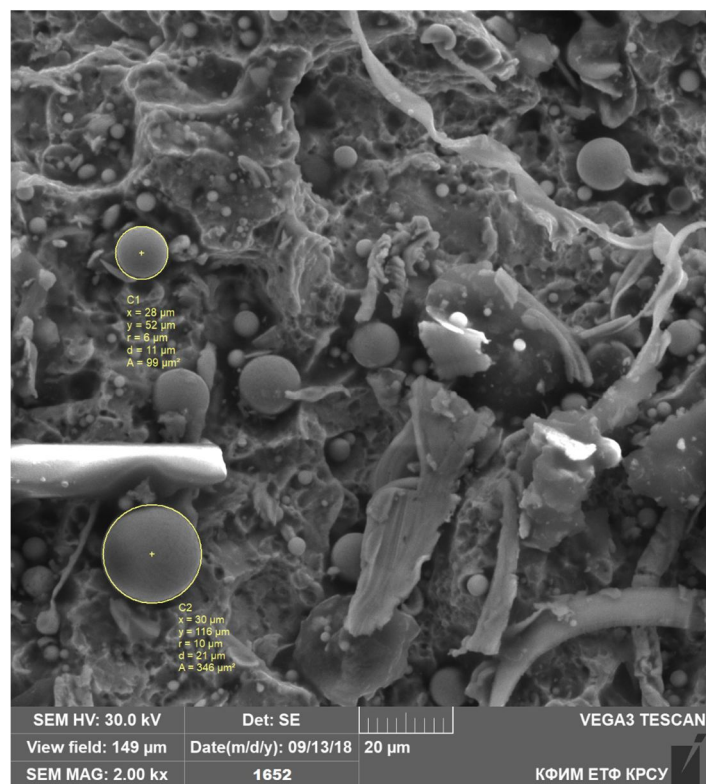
Снимок внутренней поверхности разрушенного зуба сателлита
